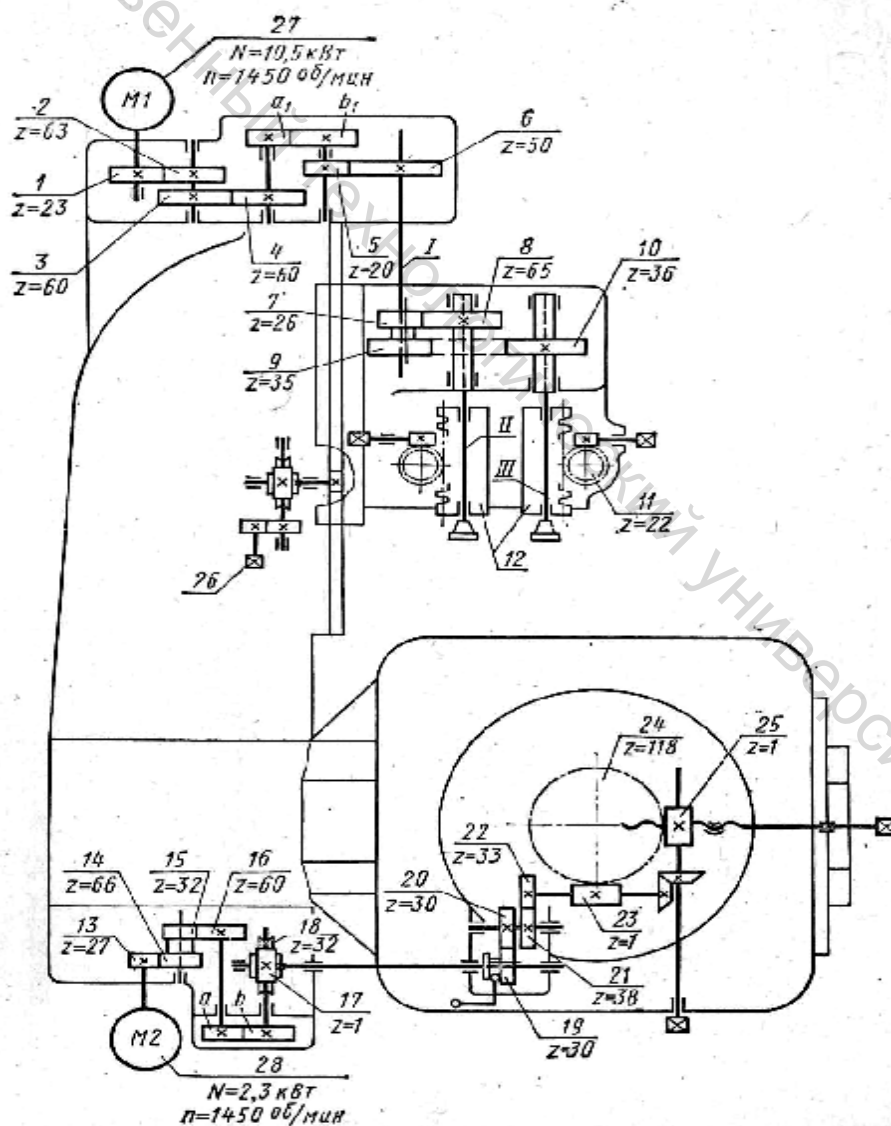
Кинематическая схема карусельно-фрезерного станка.
